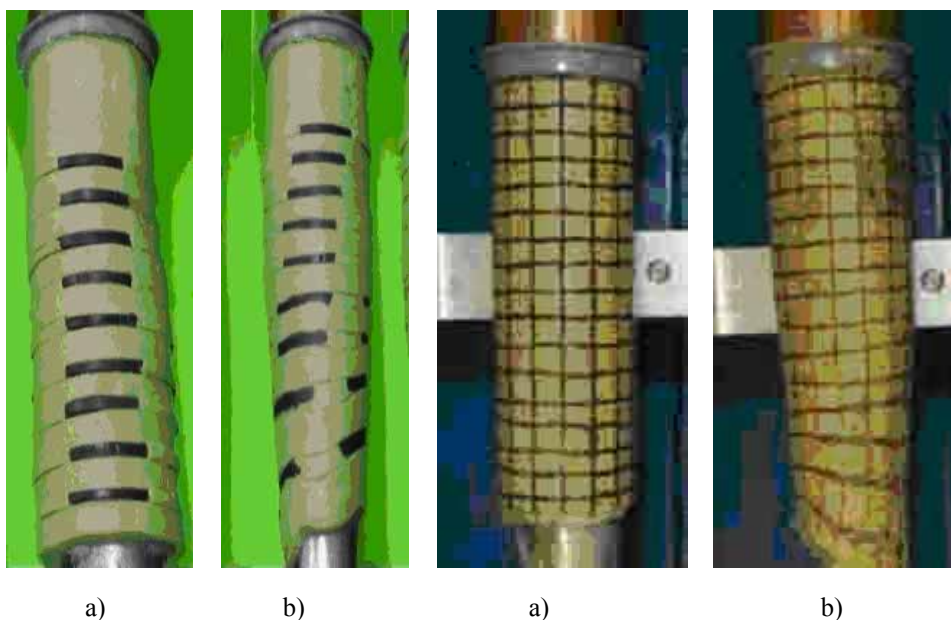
Materiał walcowany z sygnałami przed walcowaniem a) oraz po walcowaniu b)
